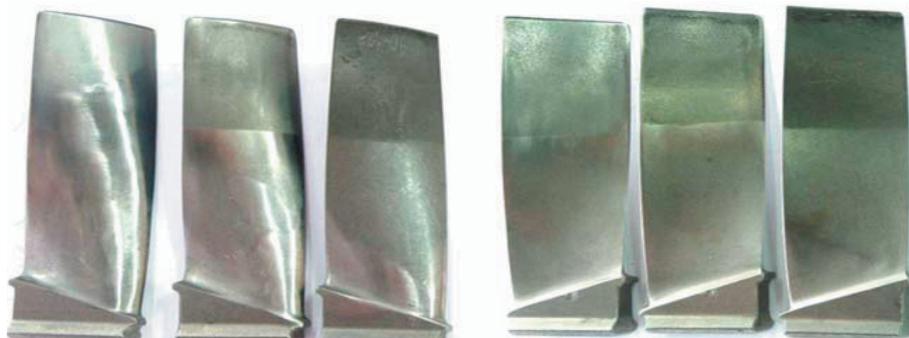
Внешний вид лопаток со стороны спинки и корыта
